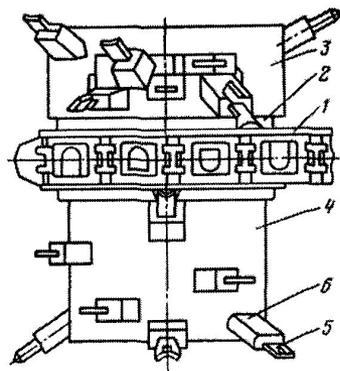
Резцовый барабанный исполнительный орган очистного комбайна:
